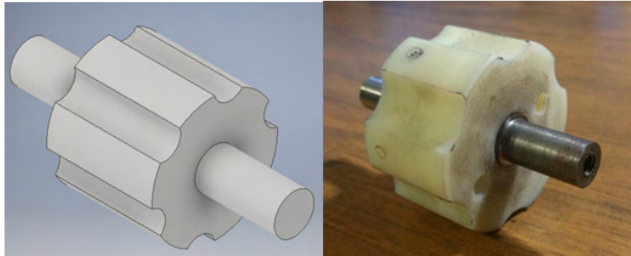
Diseño de acoplamiento (izquierda) y acoplamiento real (derecha).
